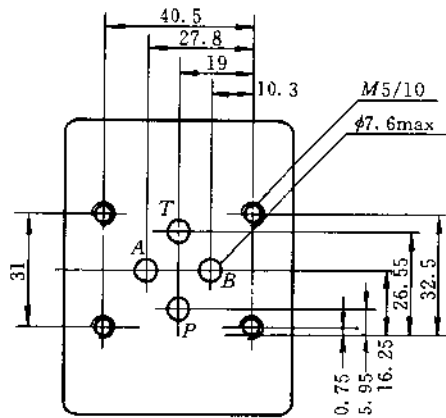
4WRE6 型直动式比例换向阀安装尺寸
